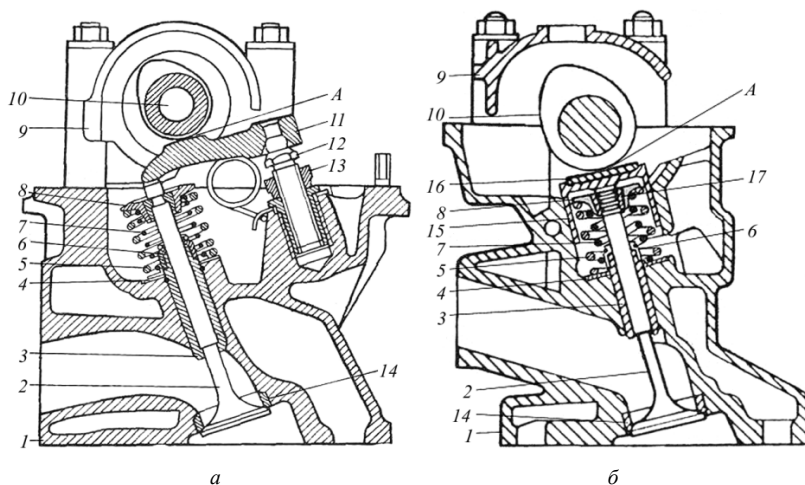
Расположение деталей клапанной группы ГРМ с рычажным приводом (а) и с цилиндрическим толкателем (б): 1 – головка цилиндров; 2 – клапан; 3 – направляющая втулка клапана; 4 – опорная шайба; 5 – пружина клапана внешняя (большая); 6 – сальник клапана; 7 – пружина клапана внутренняя (малая); 8 – тарелка пружин клапана; 9 – корпус подшипников распределительного вала; 10 – распределительный вал; 11 – рычаг клапана; 12 – упорный винт; 13 – контргайка; 14 – седло клапана; 15 – цилиндрический толкатель; 16 – регулировочная шайба; 17 – сухарь; А – регулируемый тепловой зазор
